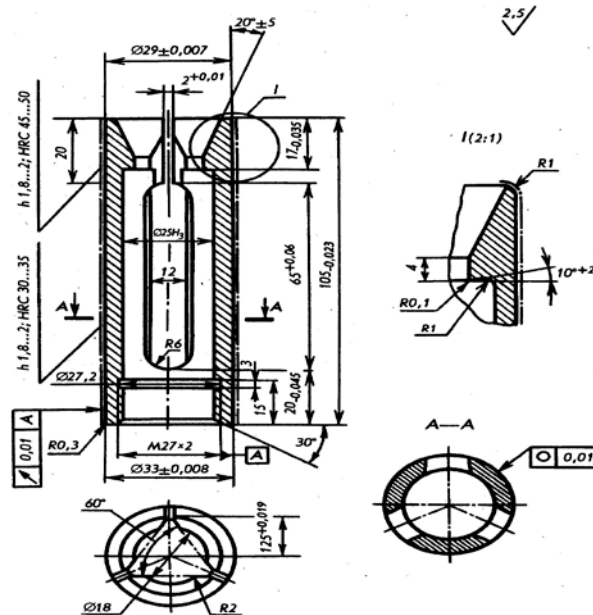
Креслення деталі з термічною обробкою поверхні.
